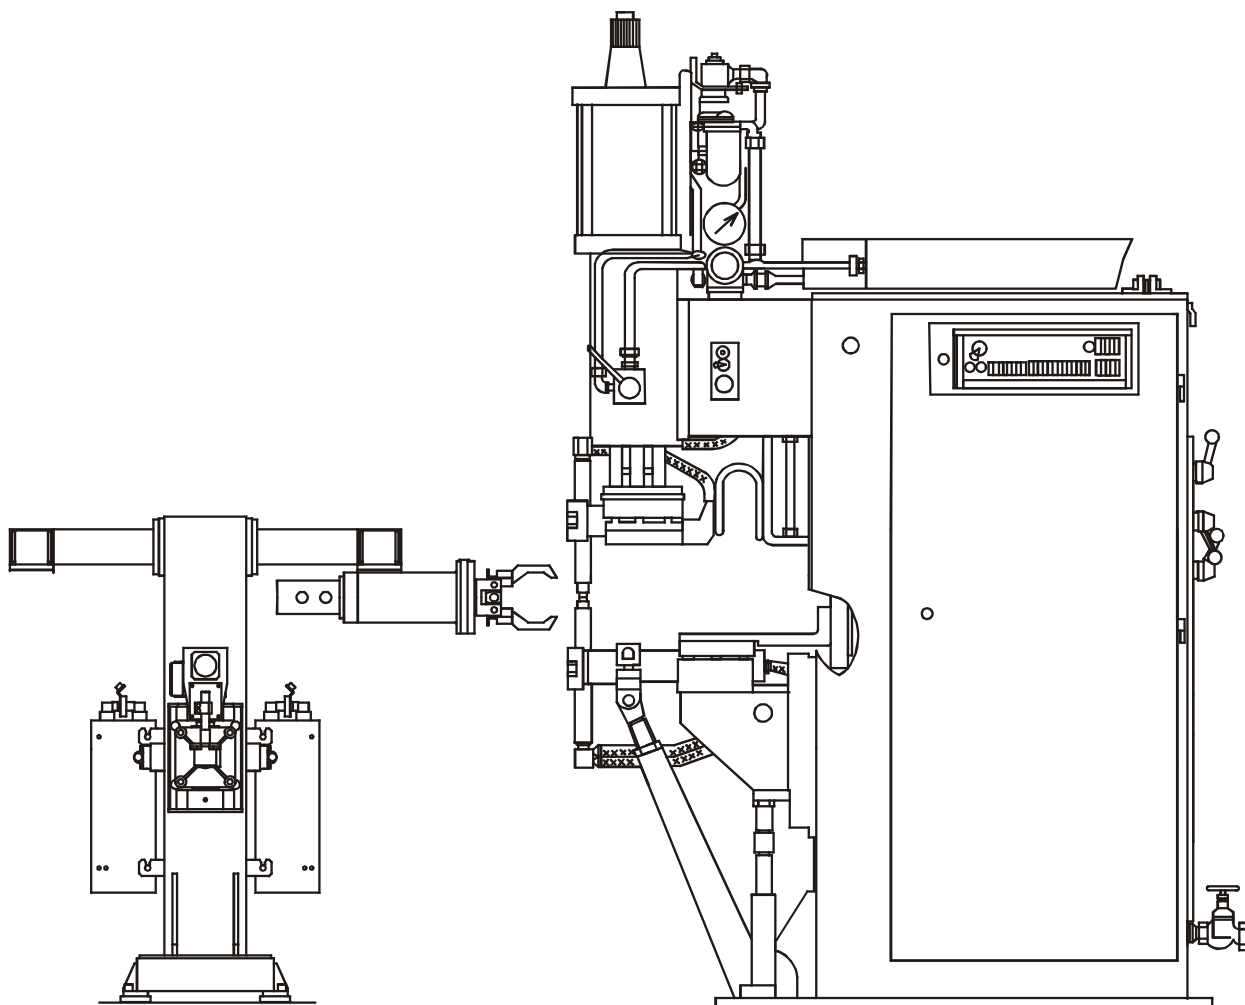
Сварка на универсальных контактных машинах с использованием механизированных и автоматизированных приспособлений
